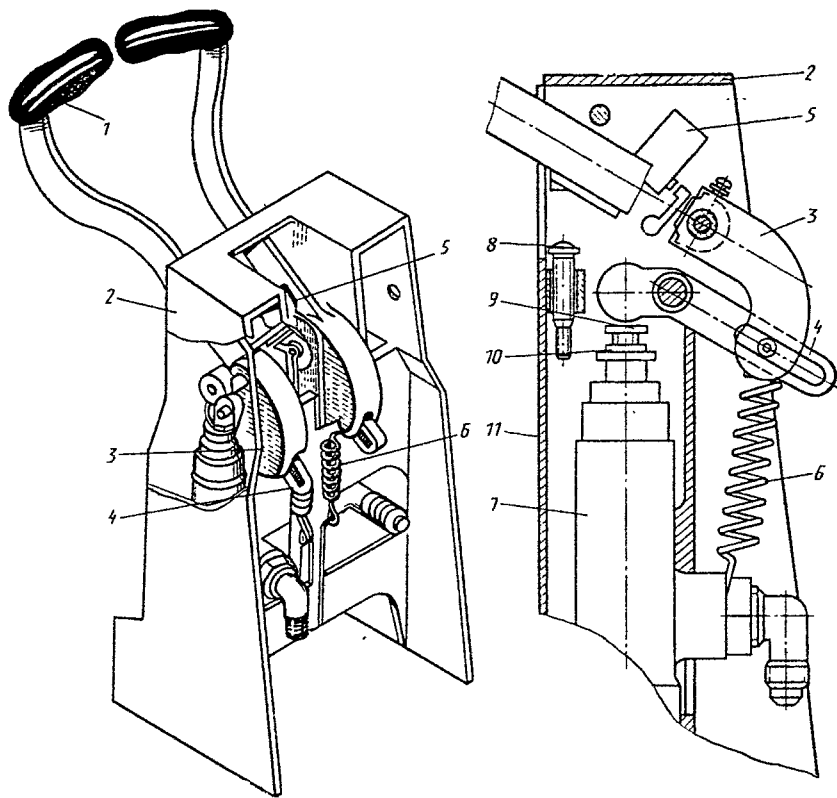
Механизм управления редукционным клапаном УГ-100 аварийного торможения: 1 — рукоятка аварийного торможения; 2 — кронштейн центрального пульта; 3, 4 — рычаги; 5 — микро-выключатель включения аварийной насосной станции; 6 — возвратная пружина; 7 — редукционный клапан УГ-100; 8 — регулировочный винт; 9 — шток УГ-100; 10 — контргайка; 11 — кожух
